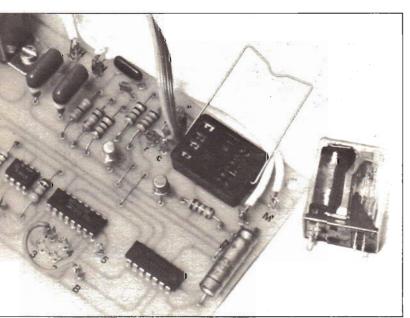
Lo zoccolo del relè può avere una staffa di fissaggio.
